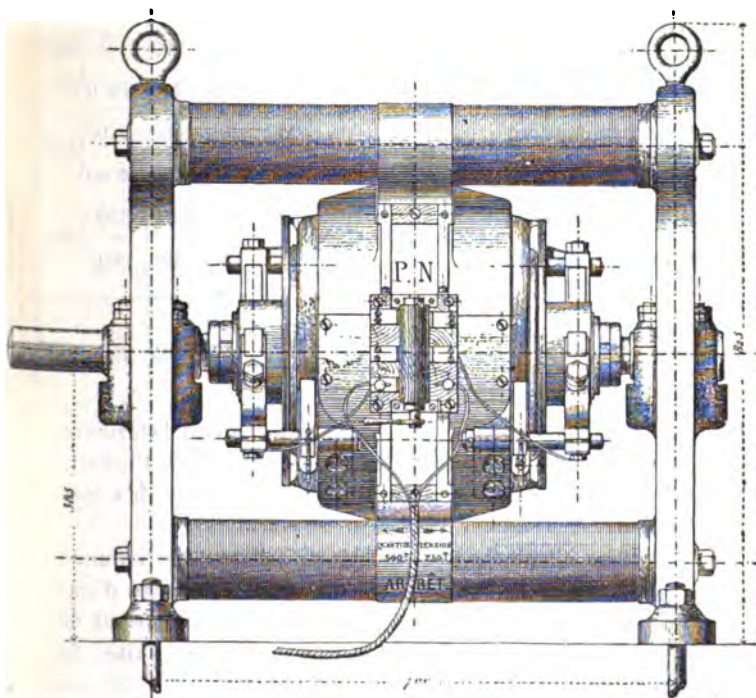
Machine de Gramme, modèle D.Q. — Ech. de 1/10.
